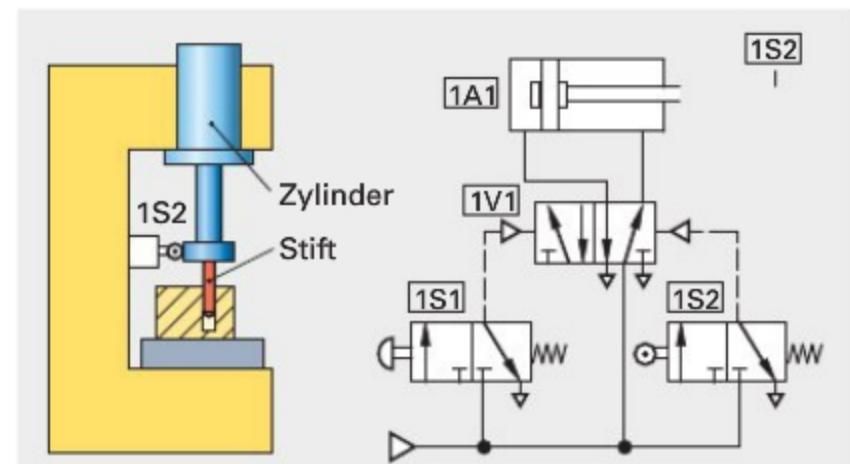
Indirekte Steuerung eines Druckluftzylinders
